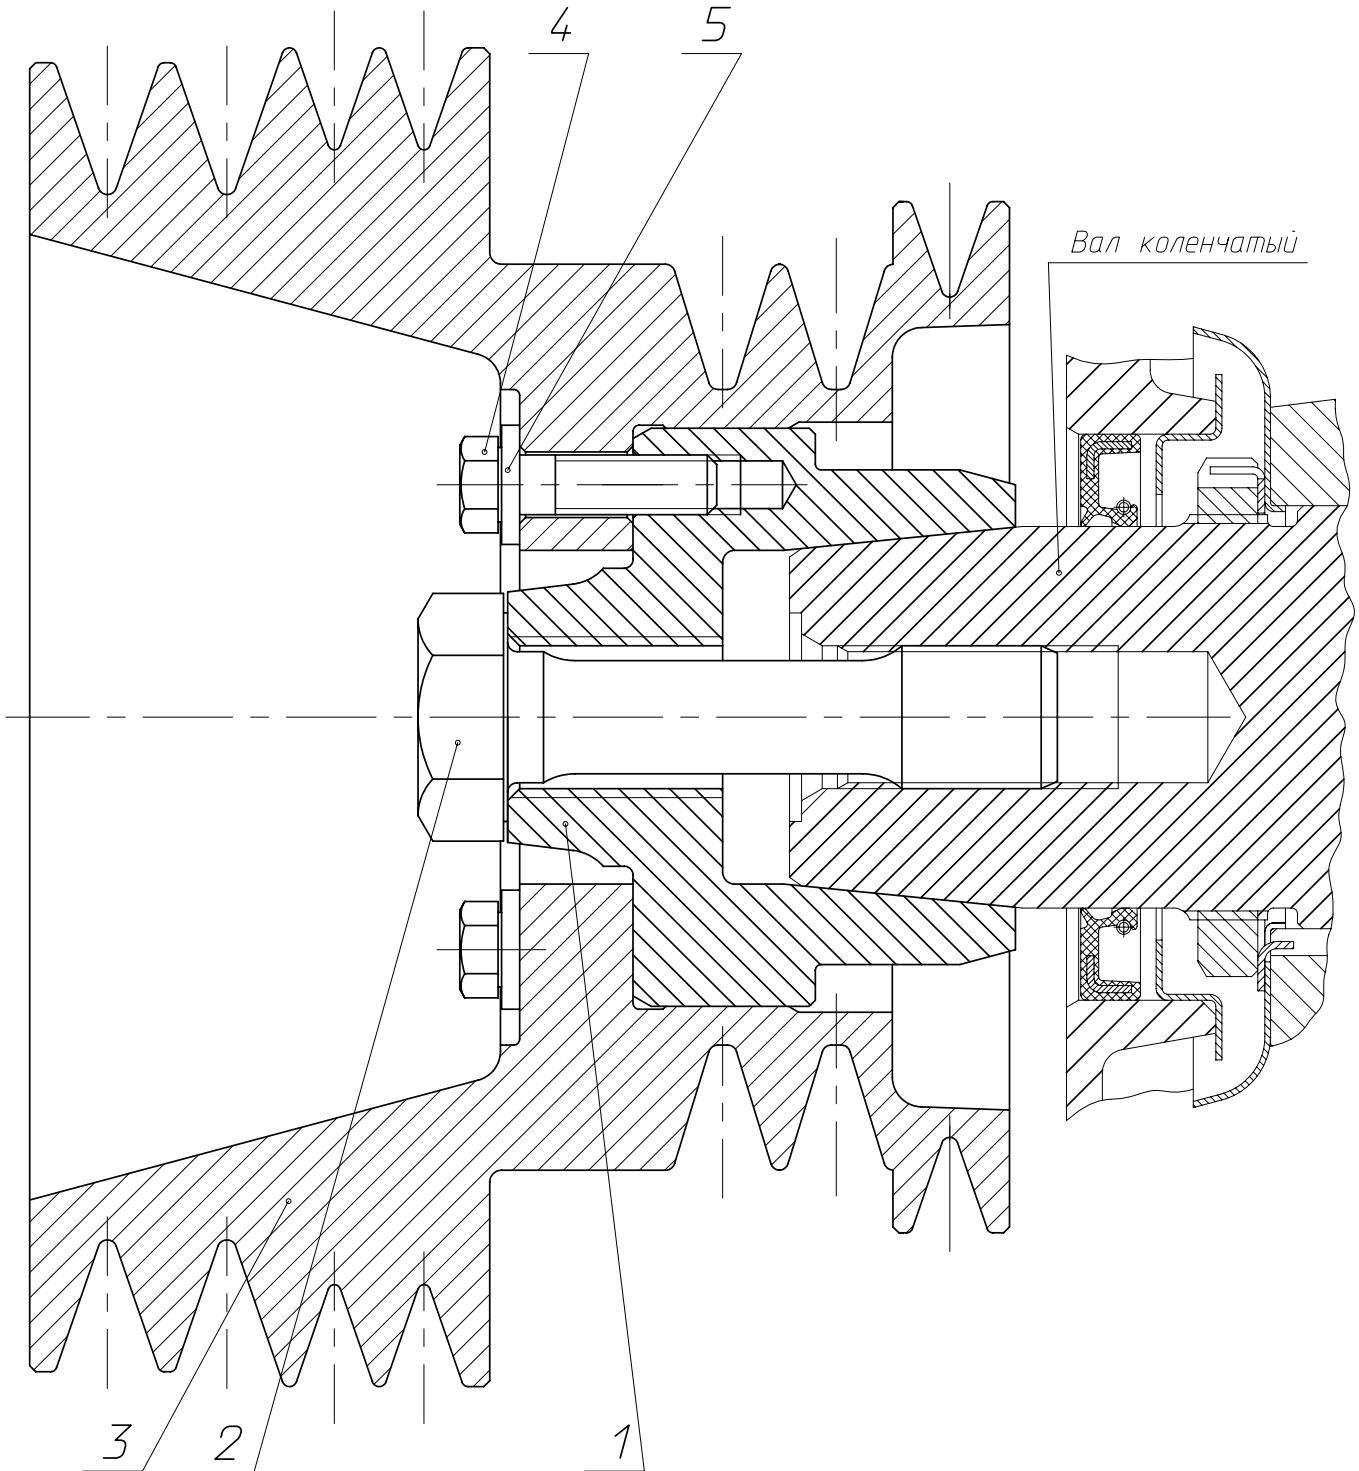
Установка шкива на двигатель, 7601.1005050
